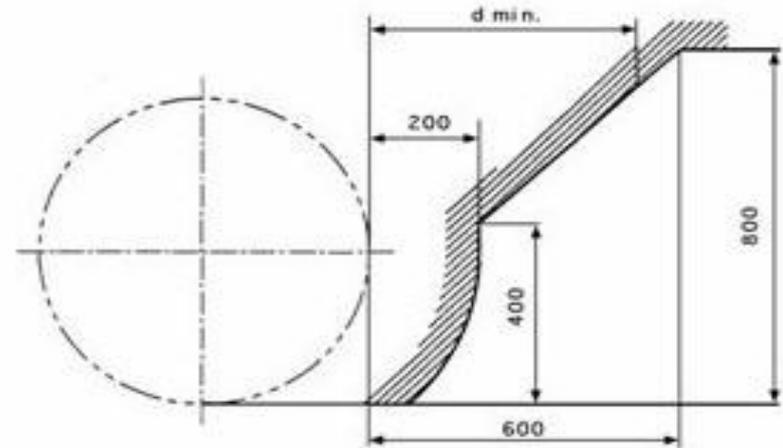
prospetto indicante le distanze di sicurezza tra la traiettoria degli utensili e il dispositivo di protezione incernierato - tratte dalla EN 708
